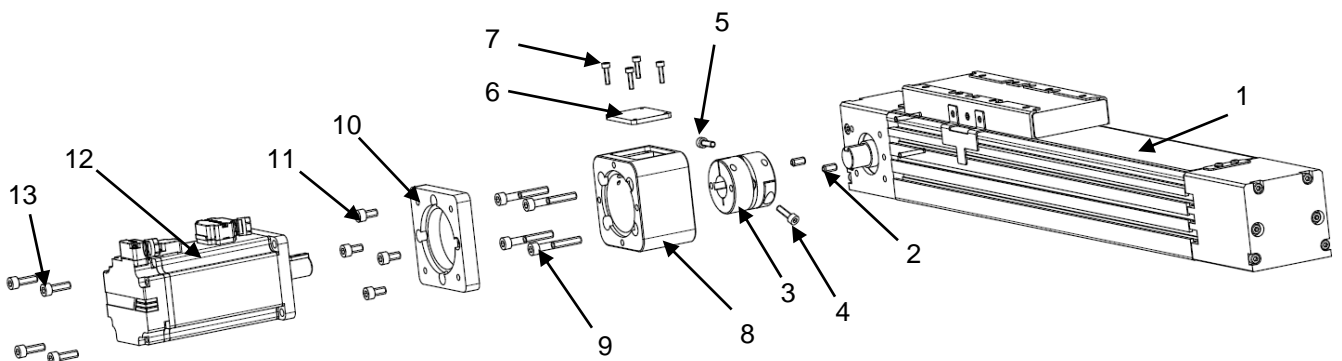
Установка двигателя/редуктора с помощью монтажного комплекта модели AM-МКCR/AR-МКCR
